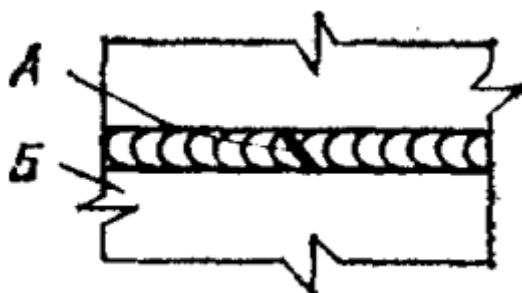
Поперечная трещина А в сварных швах стенки резервуара - сквозная или несквозная
